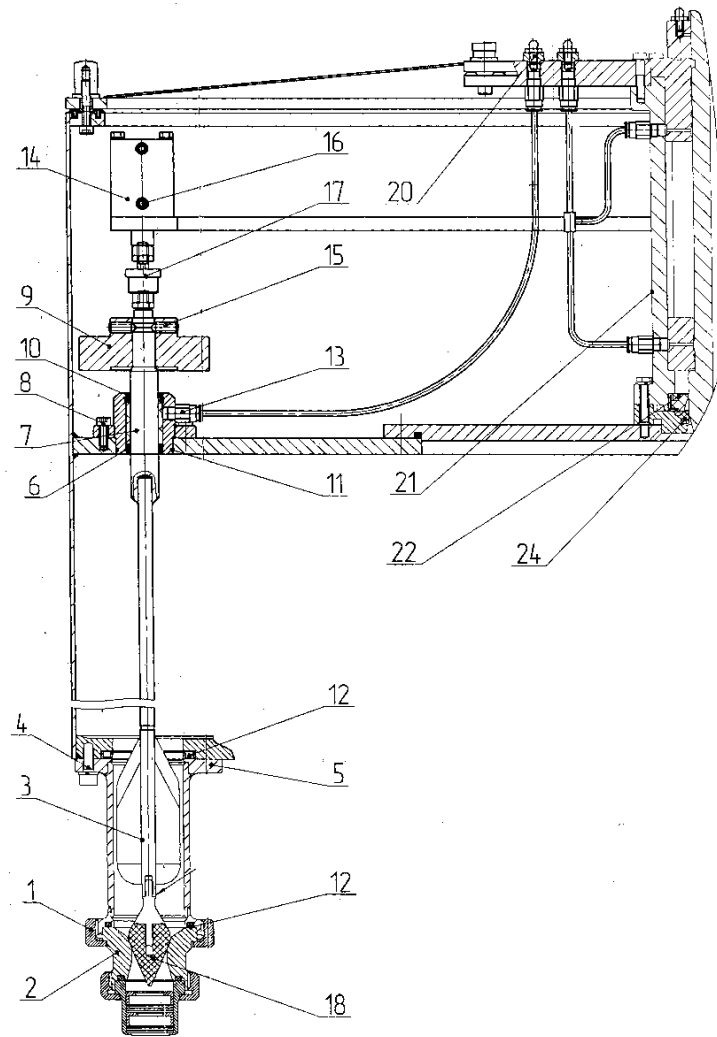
Дозувальний пристрій: 1, 19 – гайка; 2 – стакан;
